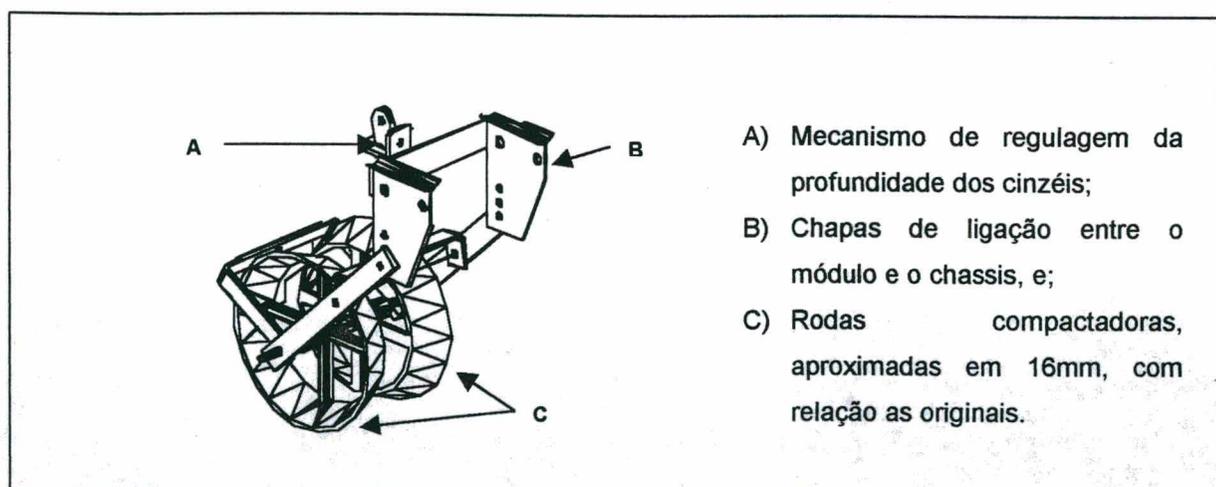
Desenho esquemático do Módulo Construtivo 05.
